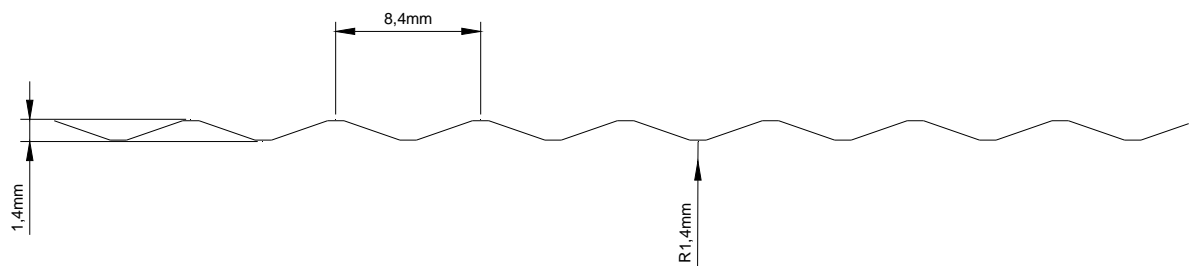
Détails de structuration de l'aluminium (ex. structure plissée)
